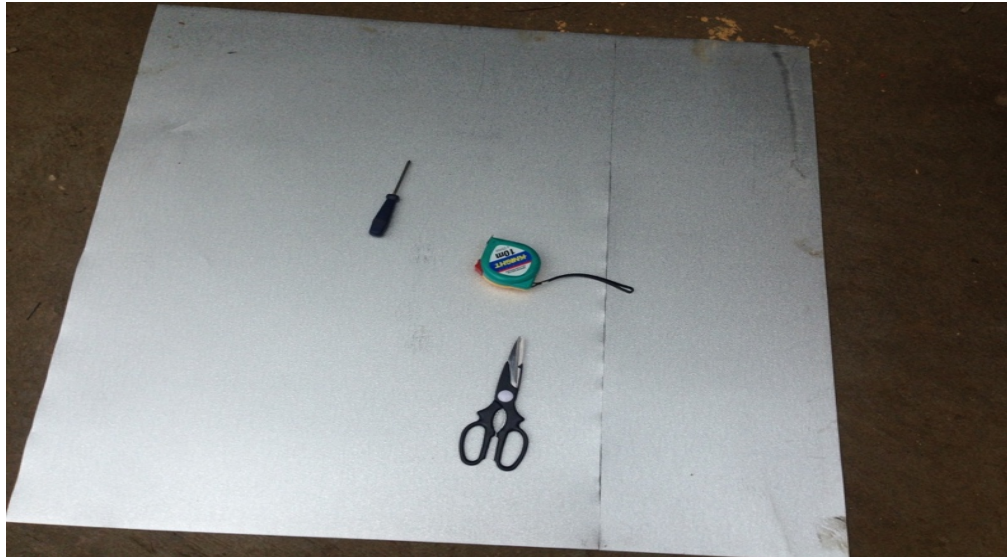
Trazado y corte de planchas de acero galvanizado. Fuente: Elaboración propia, 2016.
